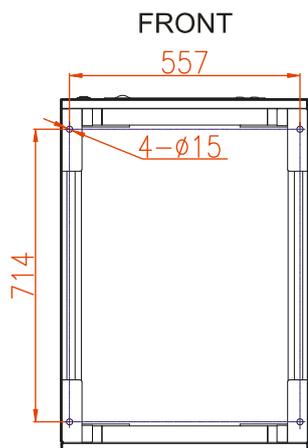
Нижний размер для MR33200, MR33300 (вид снизу) (мм)
